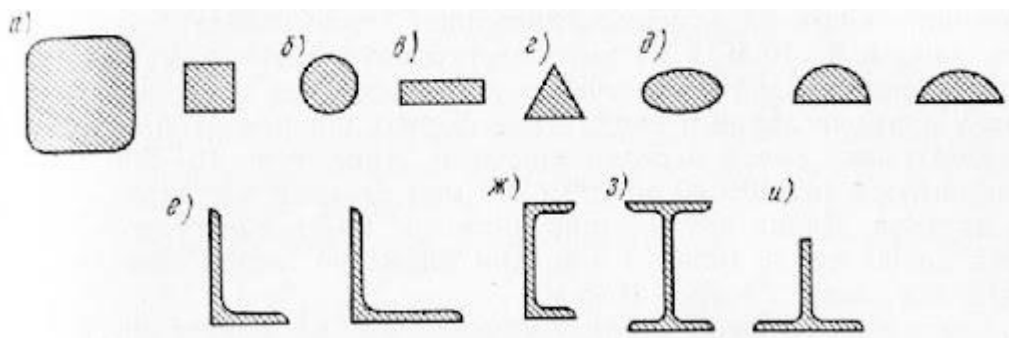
Основні види сортового прокату: а - квадратний;
